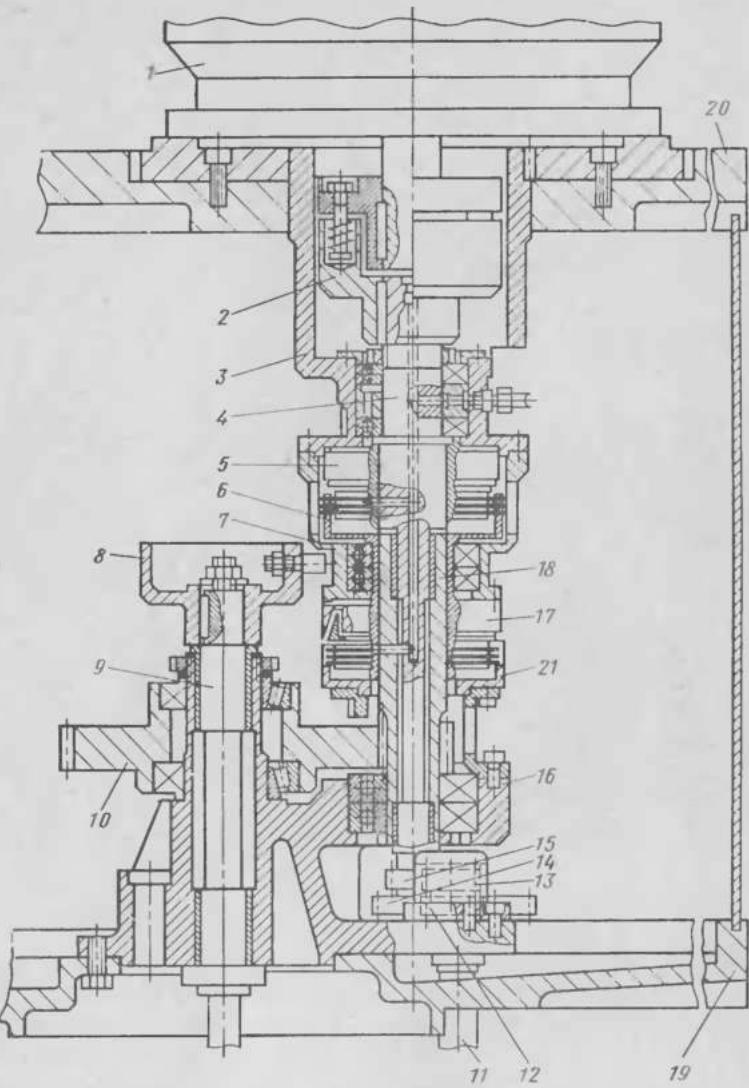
Механизм передачи движения от главного электродвигателя полуавтомата
